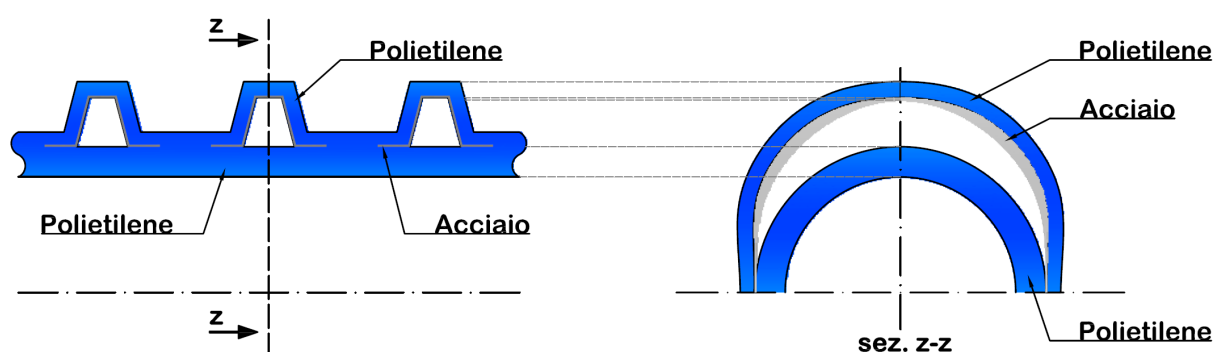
Sezione del tubo PALADEX spiralato rinforzato con acciaio.
